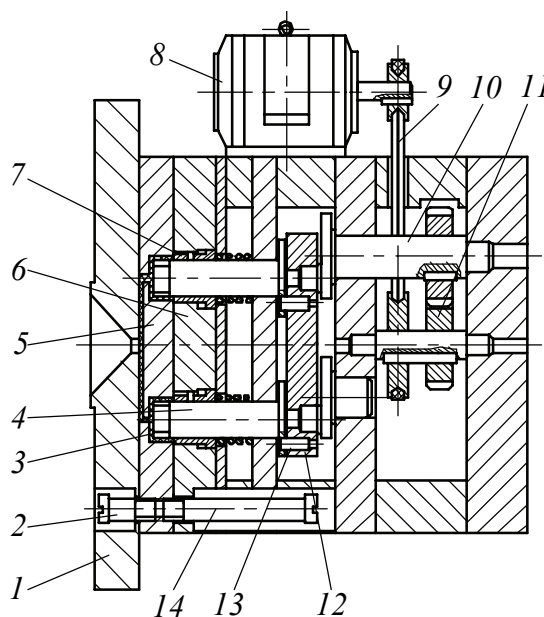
Форма для оформления резьбы на внутренней поверхности изделия с автоматическим выворачиванием резьбового знака
